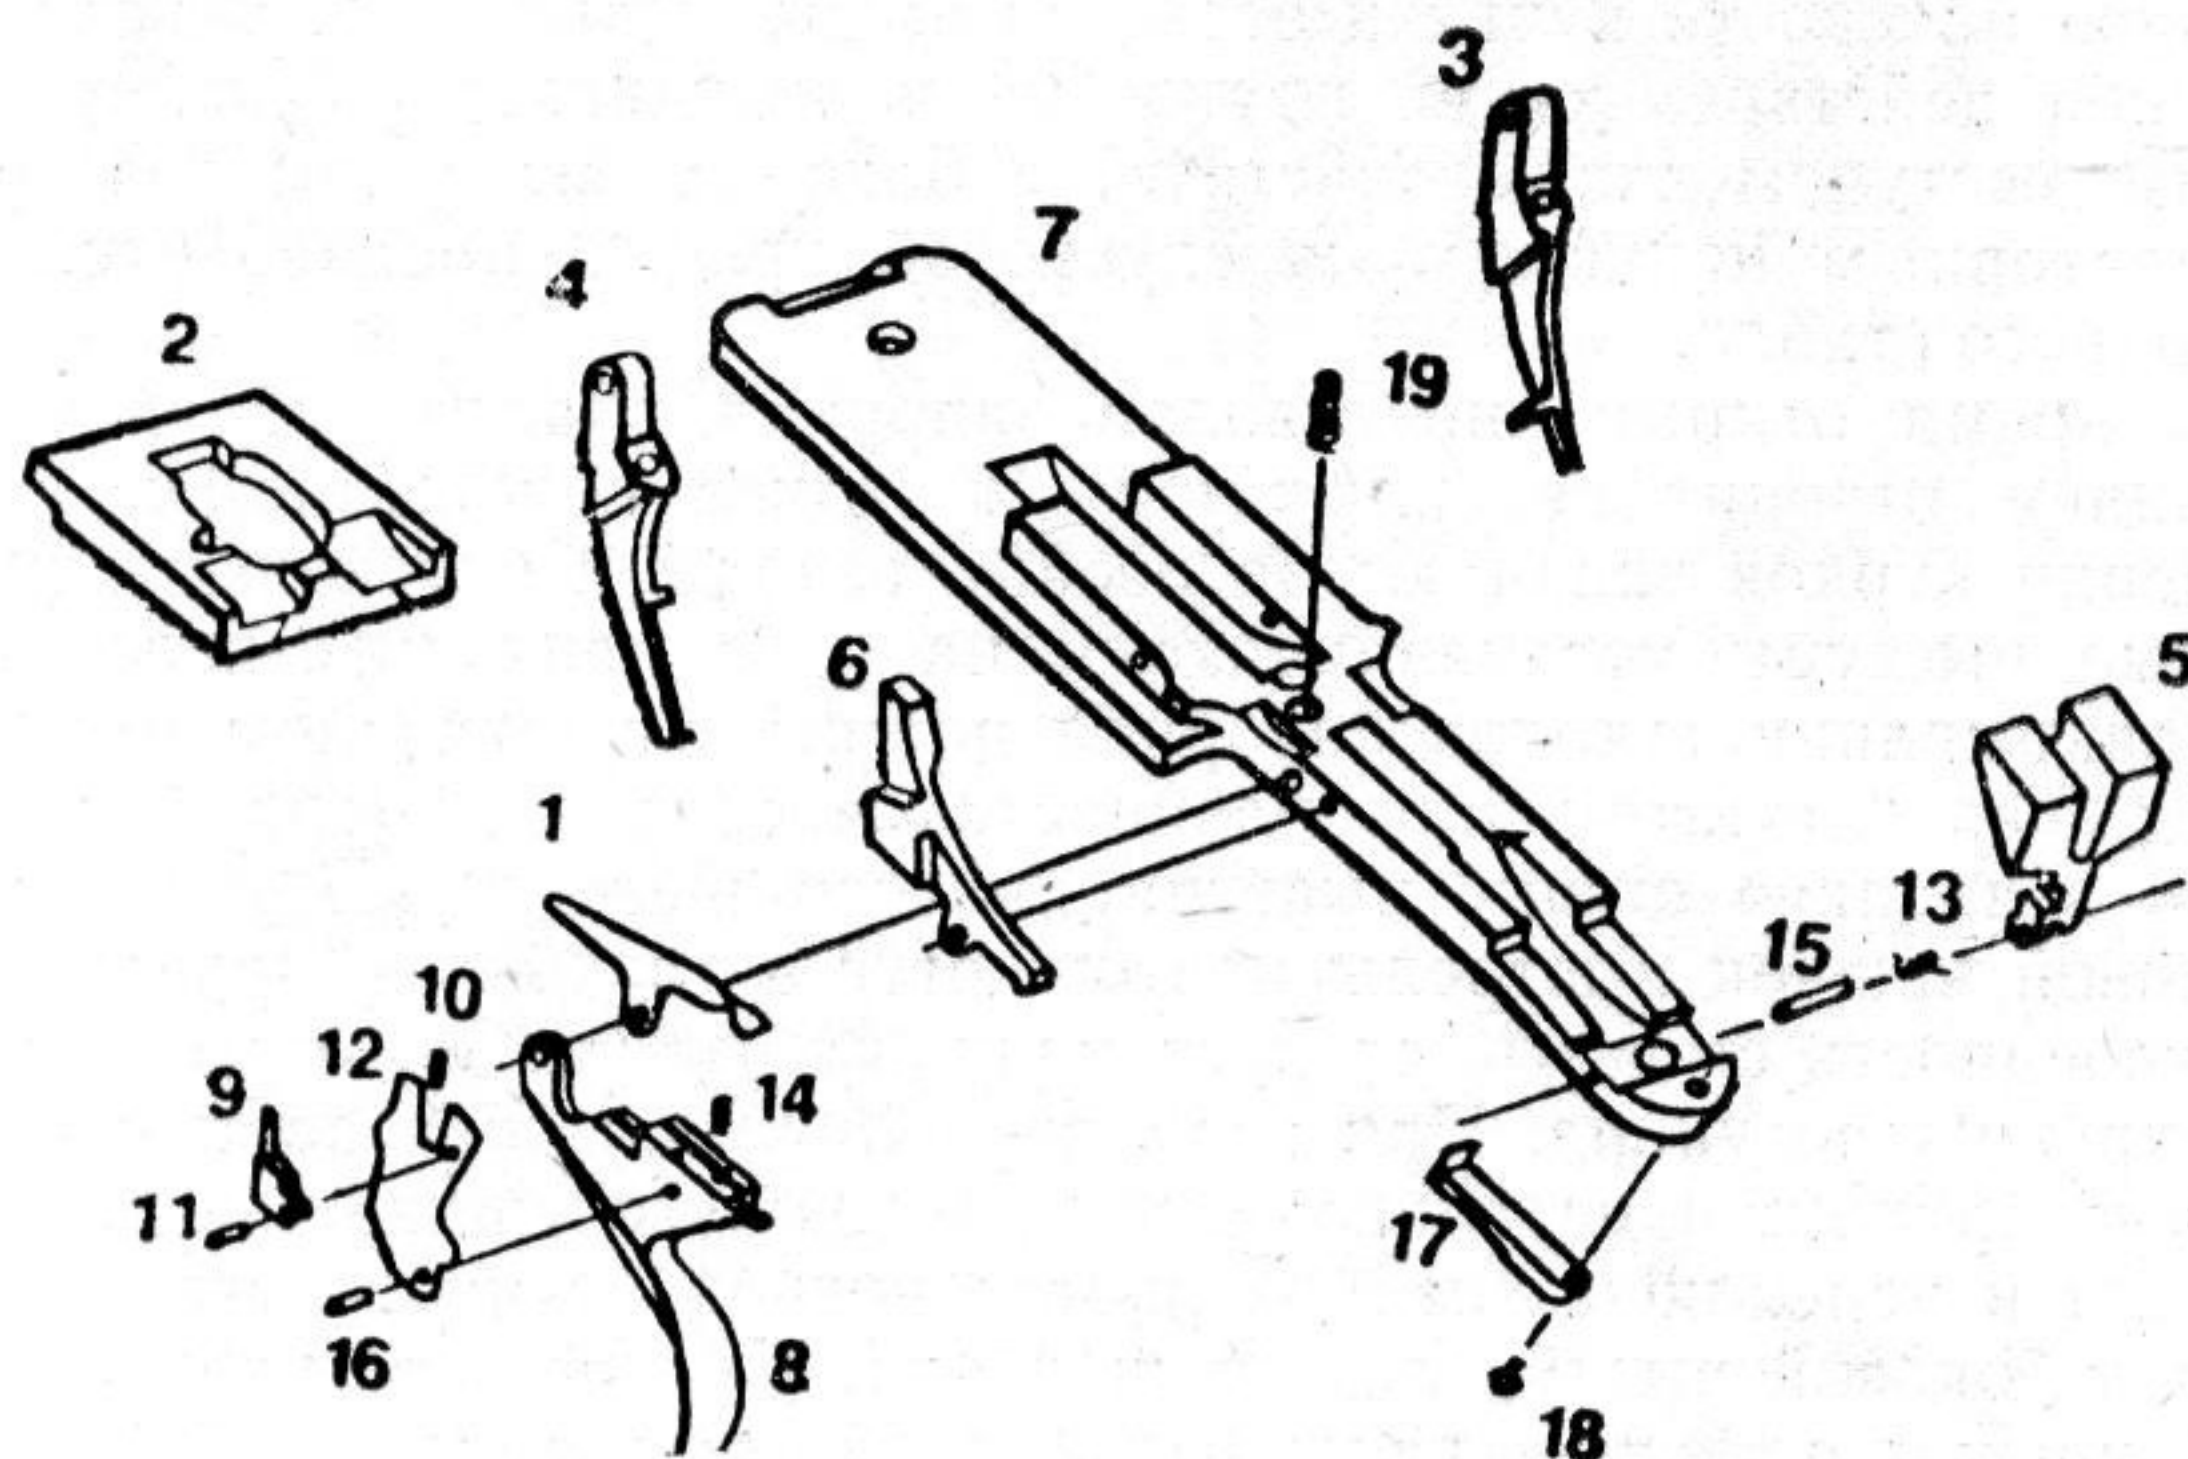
Детали спускового механизма ружья модели ИЖ-27—1С:
